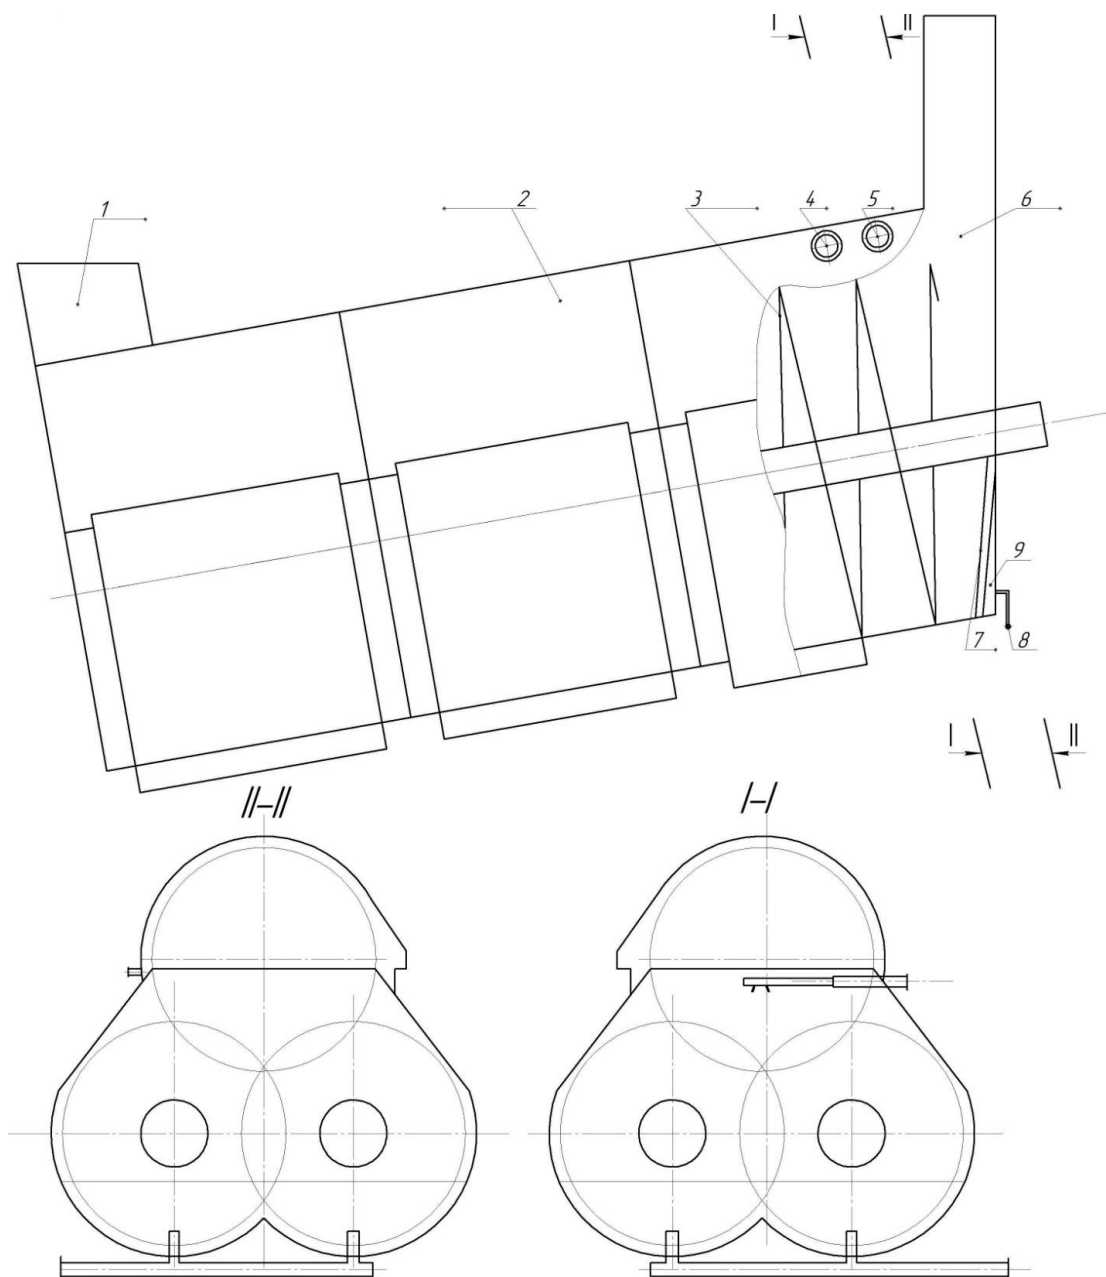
Пристрій для комбінованого підводу очищеної ЖПВ в нахилений дифузійний апарат: 1 – завантажувальна шахта; 2 – корпус апарата; 3 – шнеки; 4 – патрубок підводу ЖПВ; 5 – патрубок підводу барометричної води; 6 – черпачне колесо; 7 – нахилена стінка; 8 і 9 – відповідно патрубок та камера підводу ЖПВ
